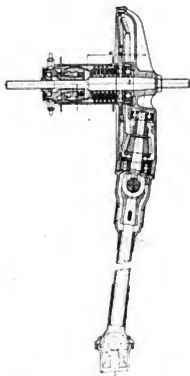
Kardantrieb des Dürkopp-Vierzylinderrades.
